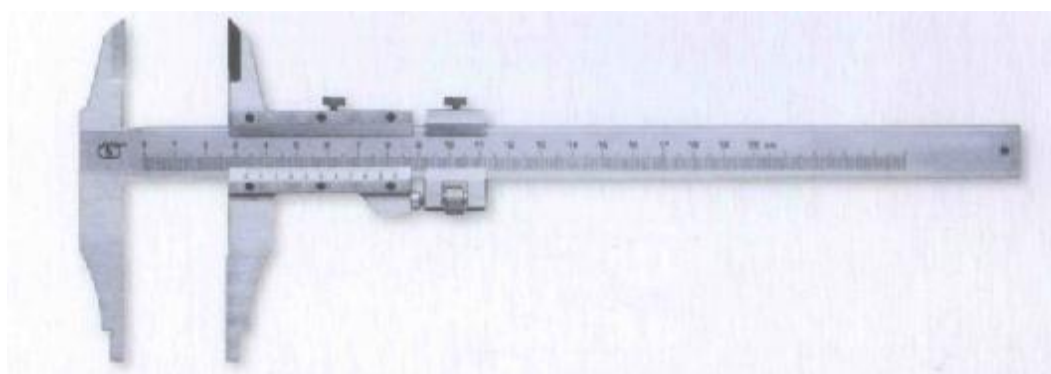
Общий вид штангенциркулей ШЦ-II
